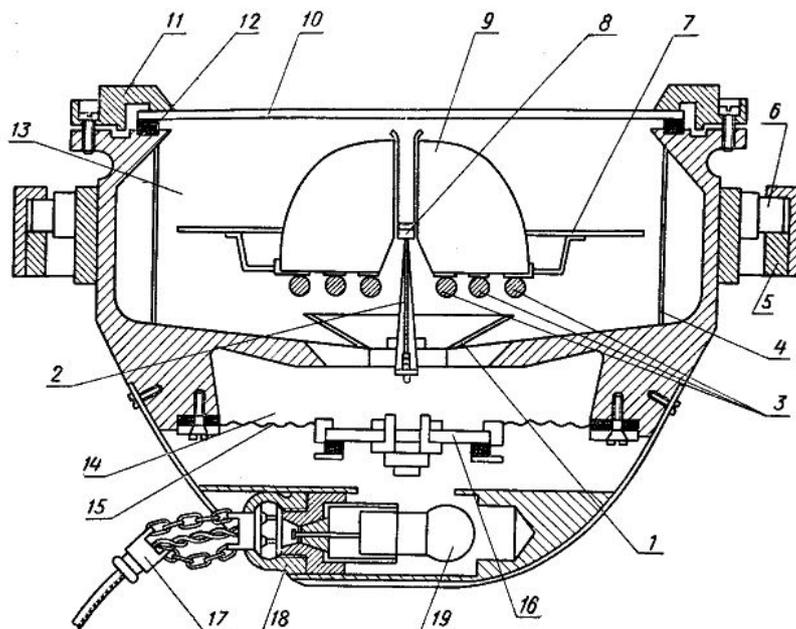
127-миллиметровый компасный котелок с донным освещением системы ГУ: 1 — отражатель света; 2 — шпилька; 3 — магнитные стрелки; 4 — курсовая черта; 5 — карданное кольцо; 6 — цапфа; 7 — картушка; 8 — топка; 9 — поплавок; 10 — стекло; 11 — азимутальный круг; 12 — резиновая прокладка; 13 — верхняя камера; 14 — нижняя камера; 15 — диафрагма; 16 — световое окно; 17 — кольцо для вытаскивания патрона; 18 — патрон; 19 — электрическая лампочка
